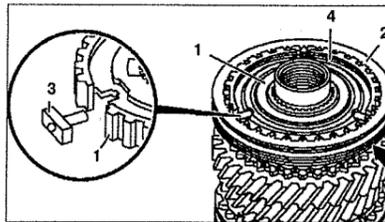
Разборка и сборка шестерни 5-й передачи (автомобили с двигателем 611.980):
